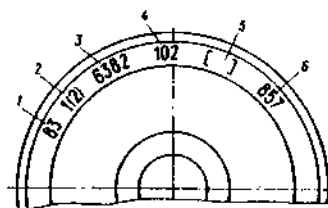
Знаки и клейма наружной боковой поверхности обода цельнокатаного колеса: 1 — год (две последние цифры) изготовления; 2 — марка стали колеса; 3 — номер
